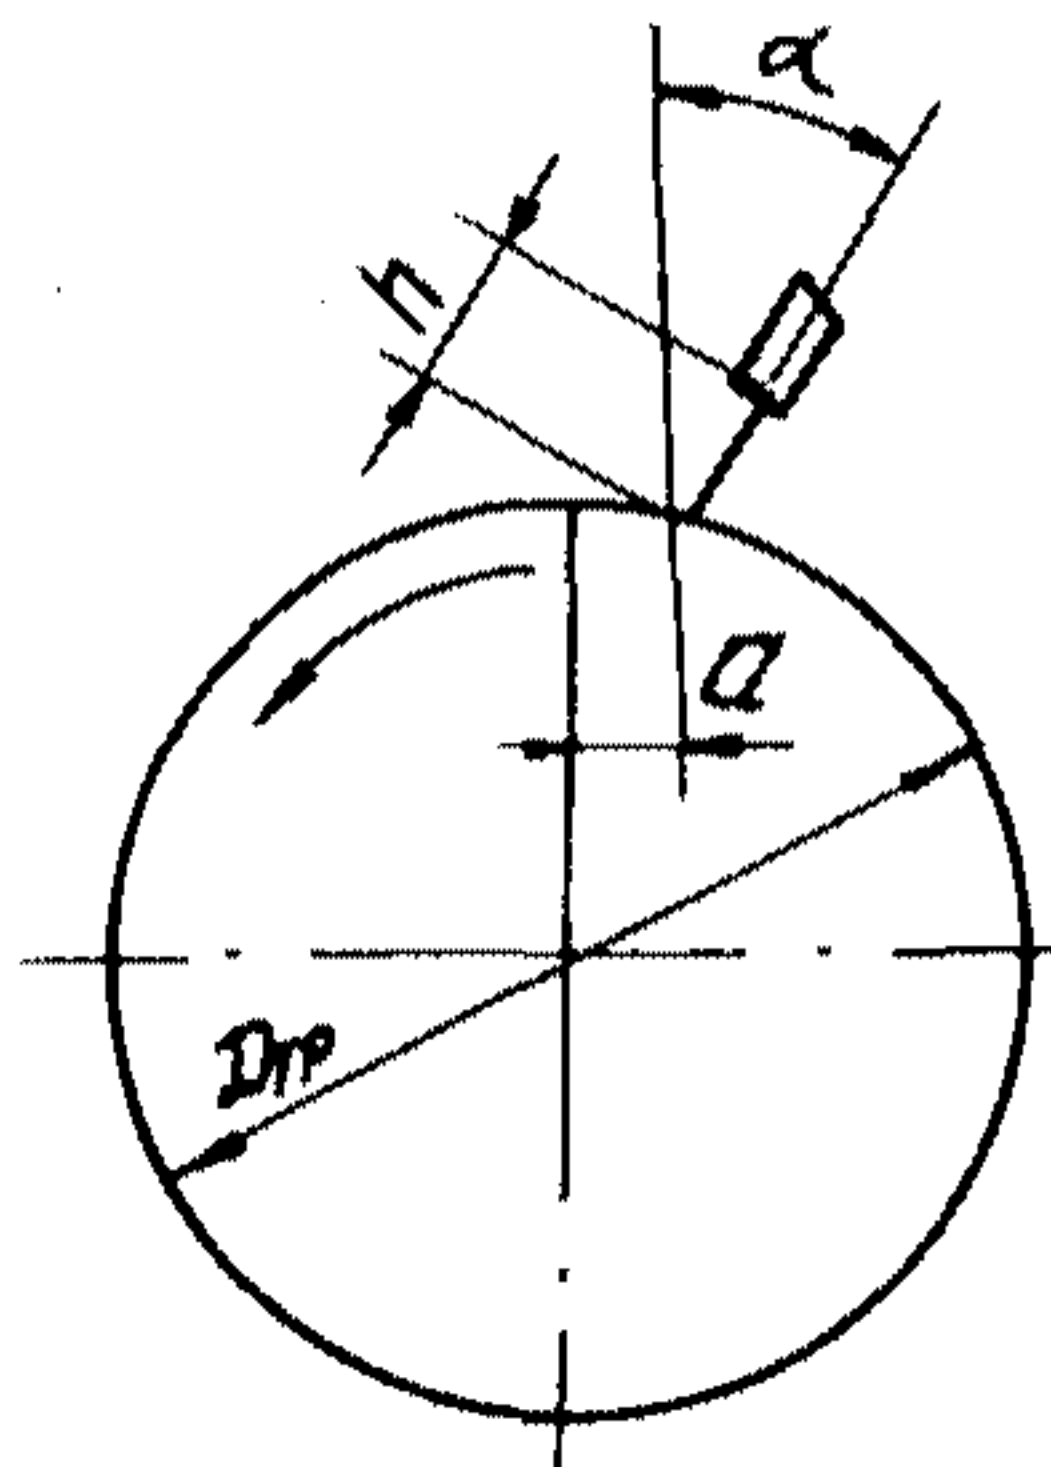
Рис. I. Положение электрода сварочной головки при автоматической сварке под флюсом поворотных стыков труб:
